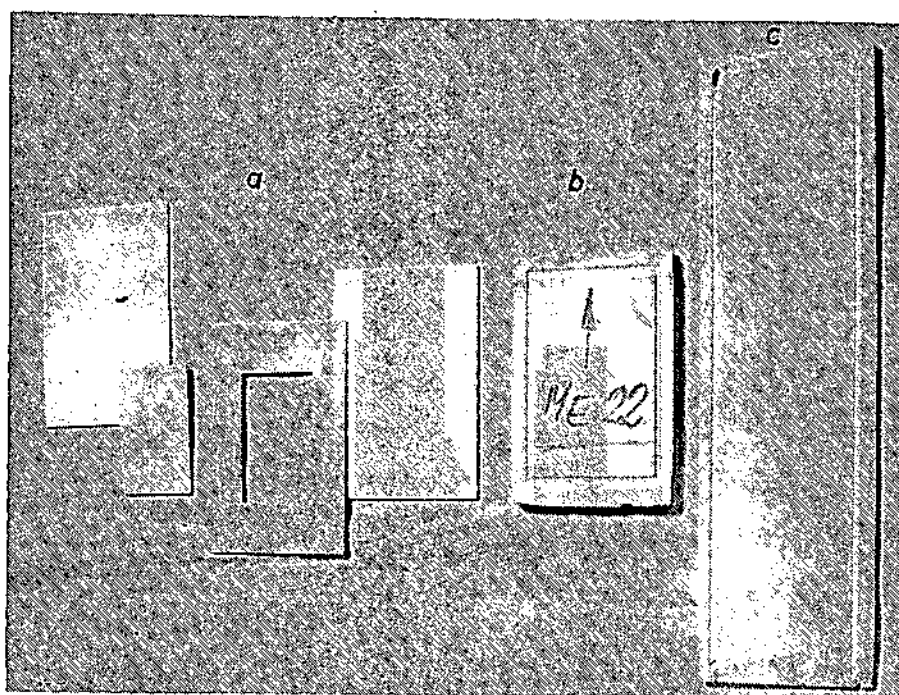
Despiece del conjunto a laminar, conjunto listo para ser laminado, conjunto laminado.
